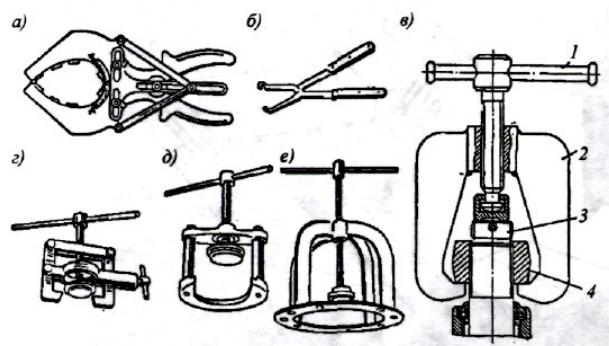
Комплект приспособлений и съемников для автомобиля ЗИЛ-130
